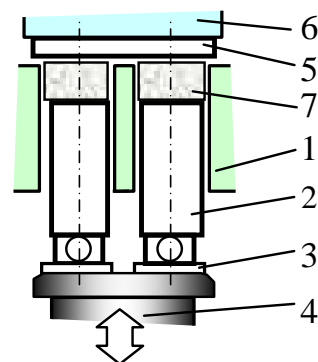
Переріз револьверного преса в зоні, де відбувається пресування: 1 – гнізда (пресформи) в столі преса; 2 – штампи; 3 – пластини регулювання висоти цегли, прикріплені до поршня механізму пресування 4; 4 – поршень механізму пресування; 5 – контрштамп; 6 – траверса; 7 – сформована цегла (сирець)
